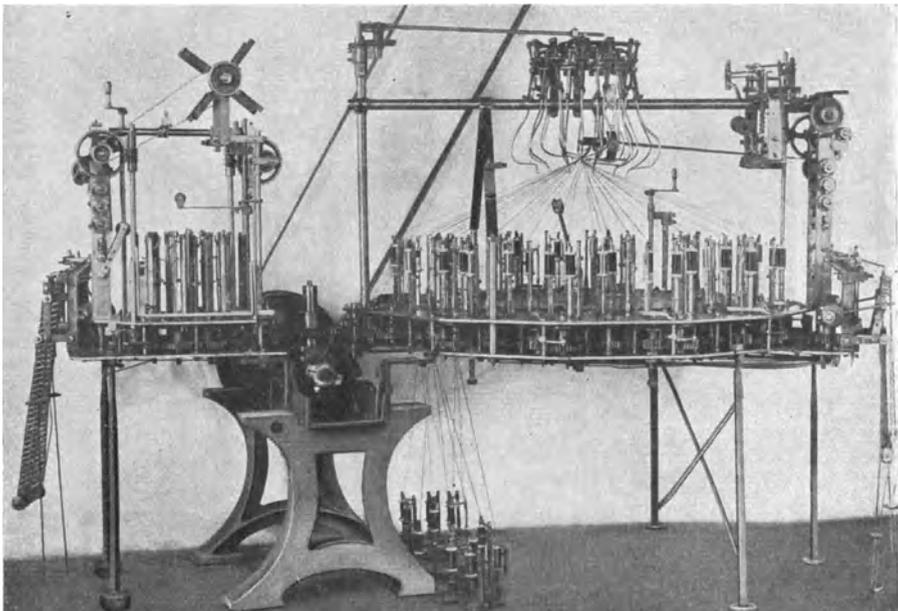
Zweiseitiger Antriebstisch für 2 Maschinen.
